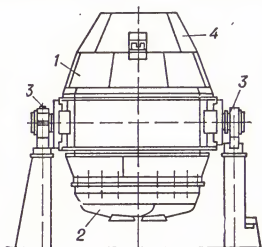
Кислородный конвертер: 1 — корпус; 2 — дно; 3 — опорные подшипники; 4 — шлем.
